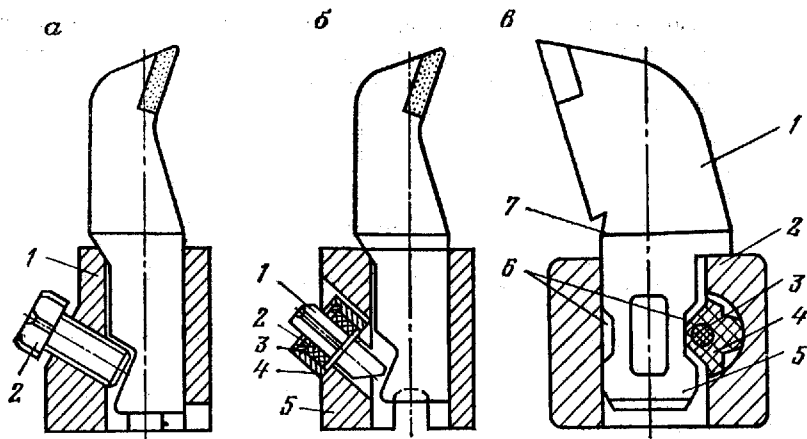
Способы крепления резцов в резцедержателях: а — резьбовое; б — фиксатором; в — упругим фиксатором
